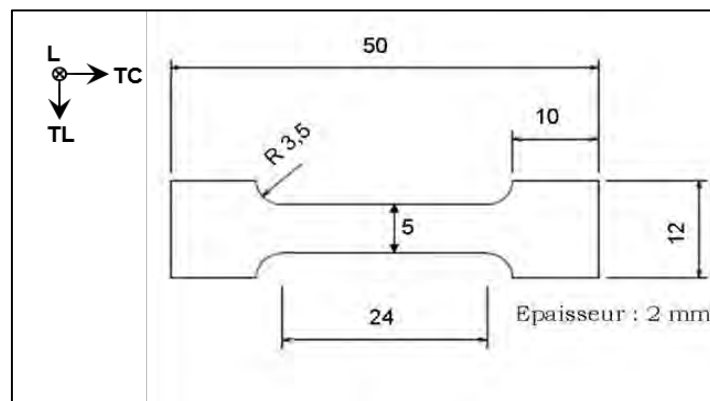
Dimensions des éprouvettes de traction utilisées
